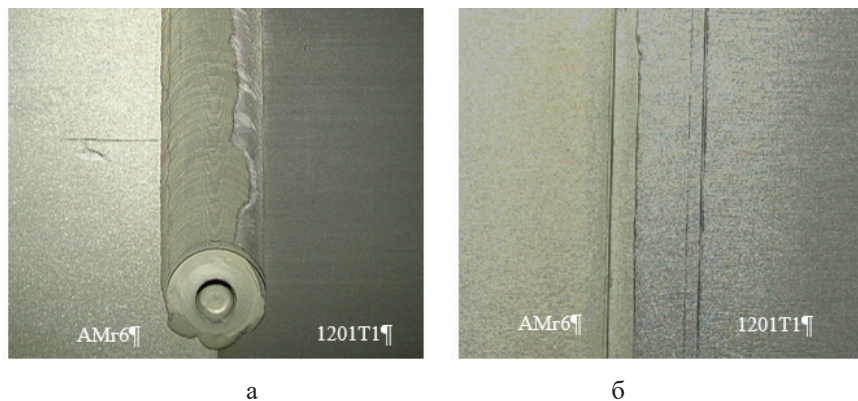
Внешний вид сварного соединения листов сплавов АМгб и 1201Т1 с лицевой (а) и обратной (б) стороны. После СТП образец анодирован
